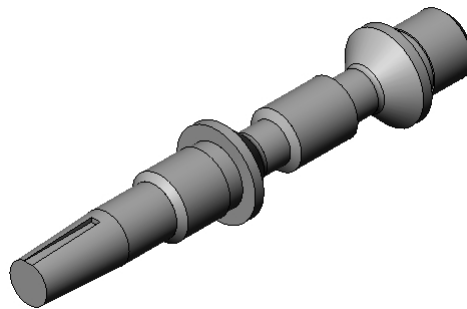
3D модель заготовки черв'яка виконана в Solid Works
